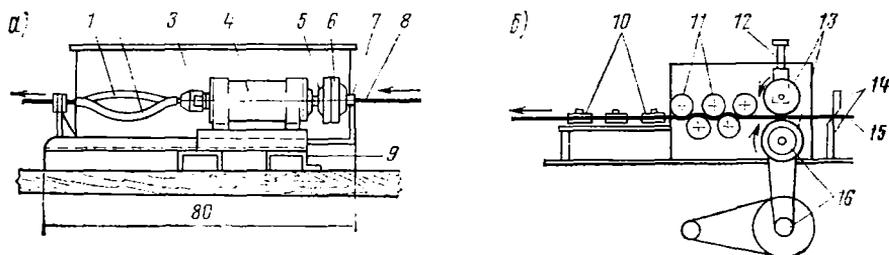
Устройство для правки проволоки и стержневой арматуры малого диаметра:
